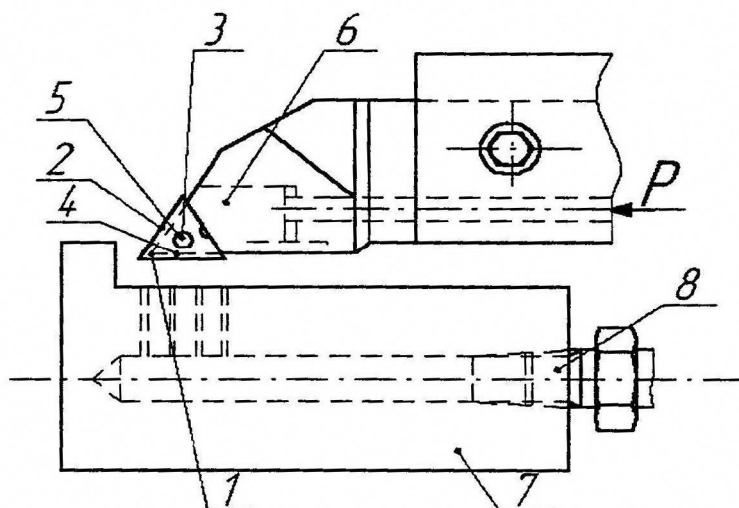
Пристрій для заміни різальних кромки з механізмом для промивання різального інструменту [2]
